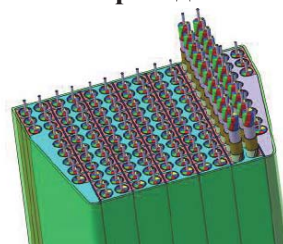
Конструкция катушки тороидального поля со сверхпроводниками ИТЭР
